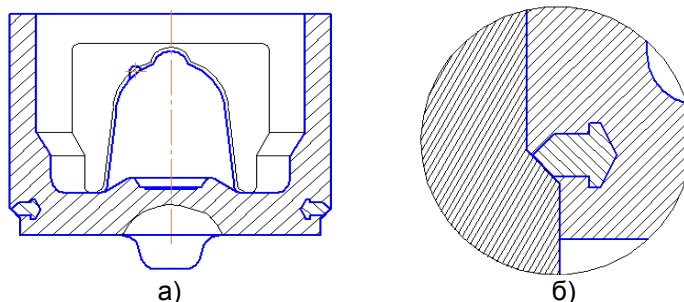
Литая заготовка поршня (а); сечение поршня в месте установки нирезистовой вставки (б)
